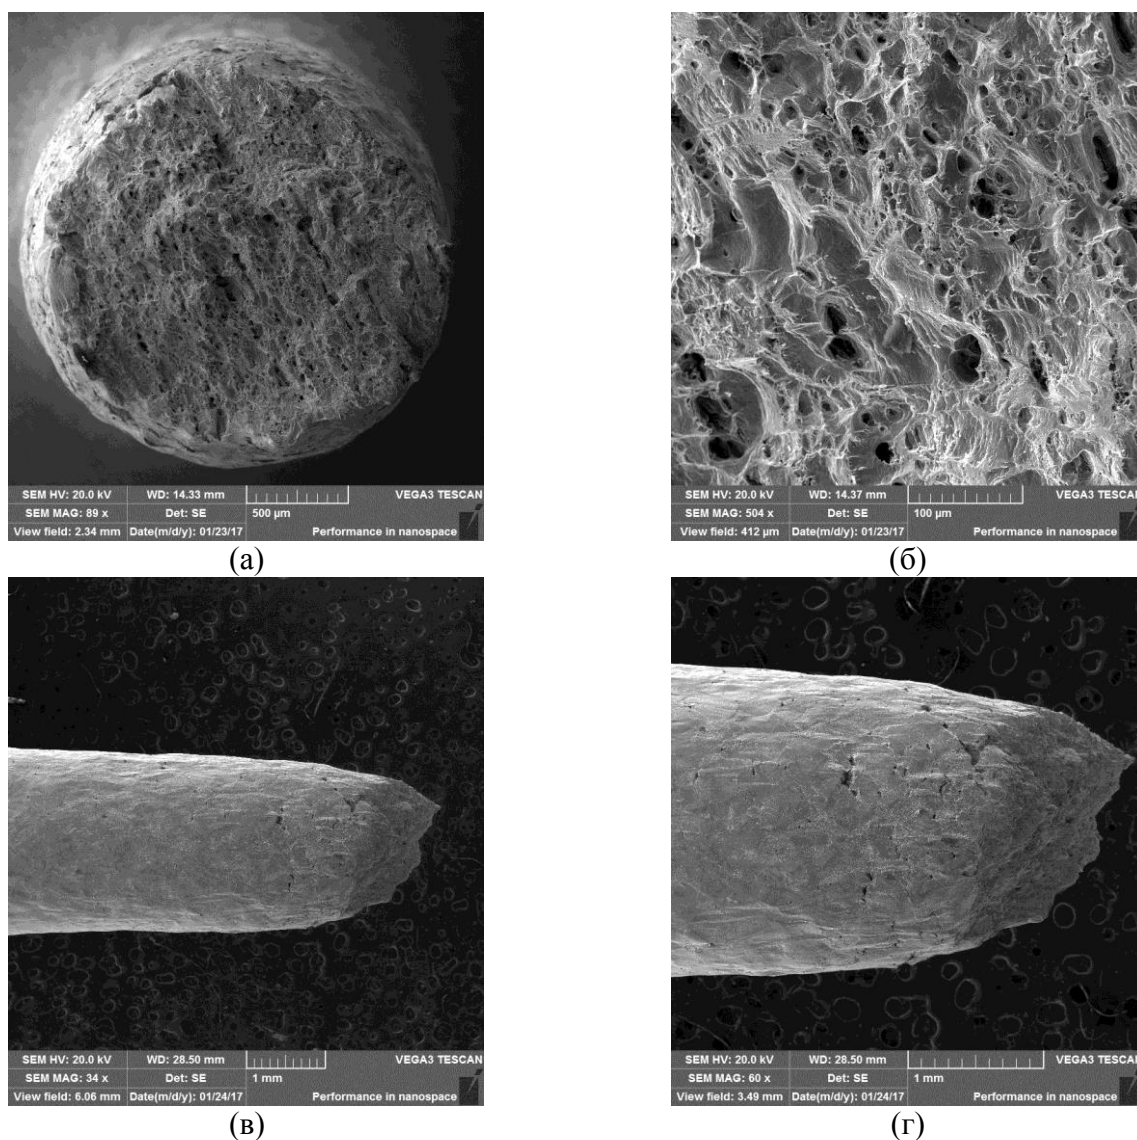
Поверхность разрушения и боковая поверхность полированного образца из стали 08X18N10T в состоянии «Т», испытанного в среде, имитирующей теплоноситель I контура реактора ВВЭР (а – общий вид излома; б – вязкий чашечный излом (в середине образца); в, г – боковая поверхность)
